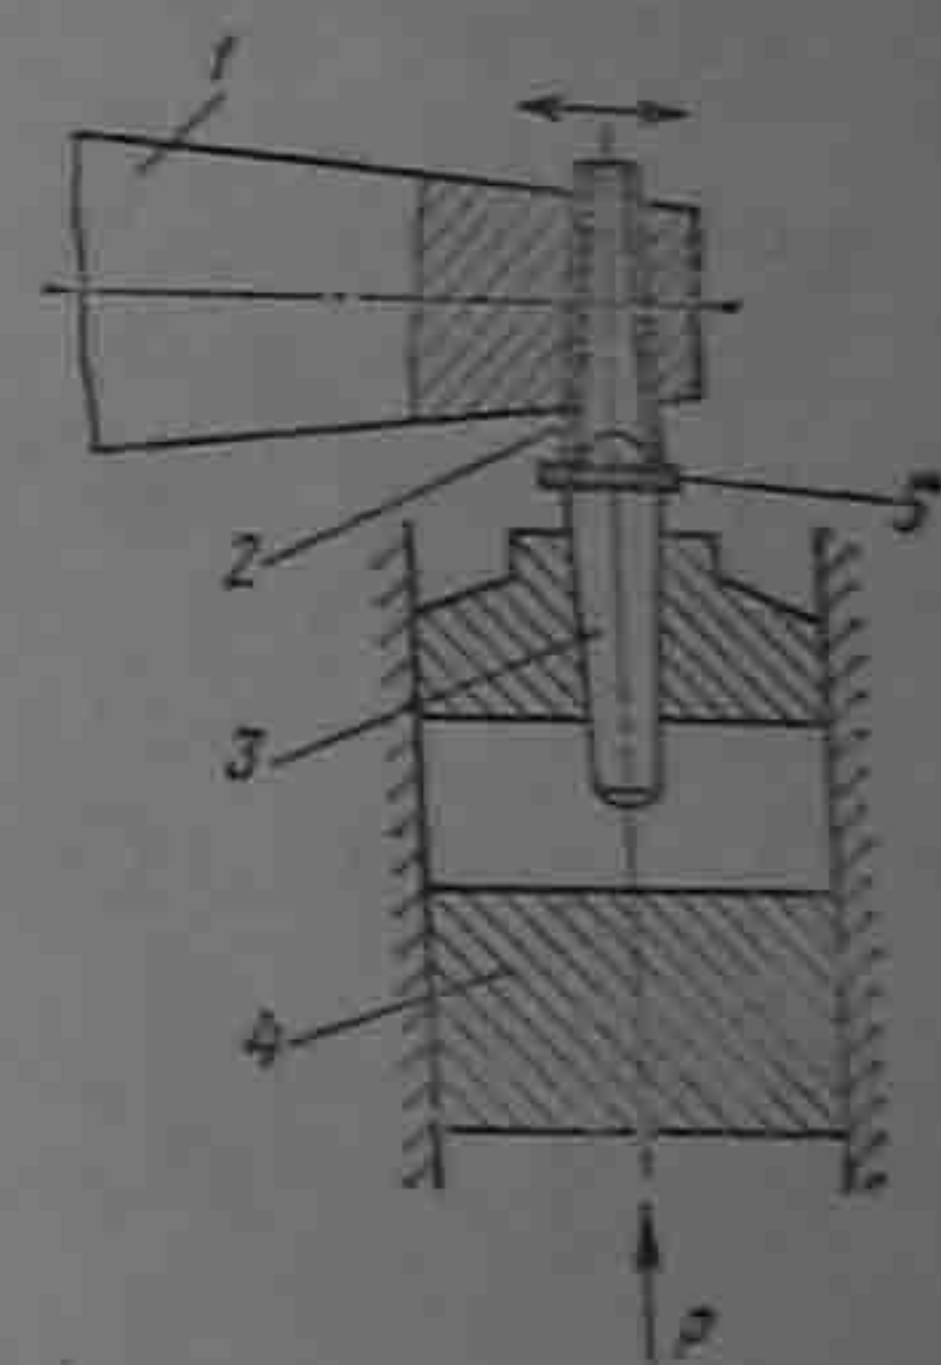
Ультразвуковая сварка по контуру:
